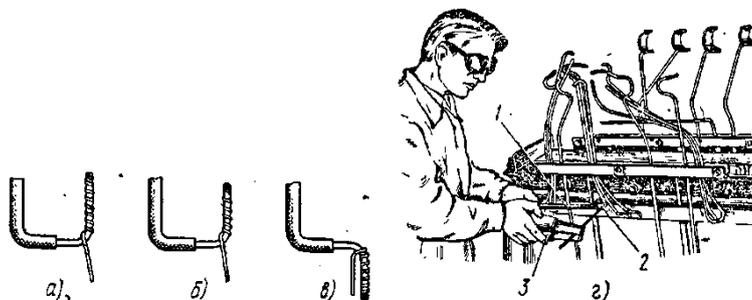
Операции сварки отводов обмотки ВН:а — подготовка к сварке, б — выполненная сварка, в — подготовка для изолирования, г — приваривание отвода к выводу обмотки; 1 — захват с крючком, 2 — привариваемый отвод, 3 — клещи
